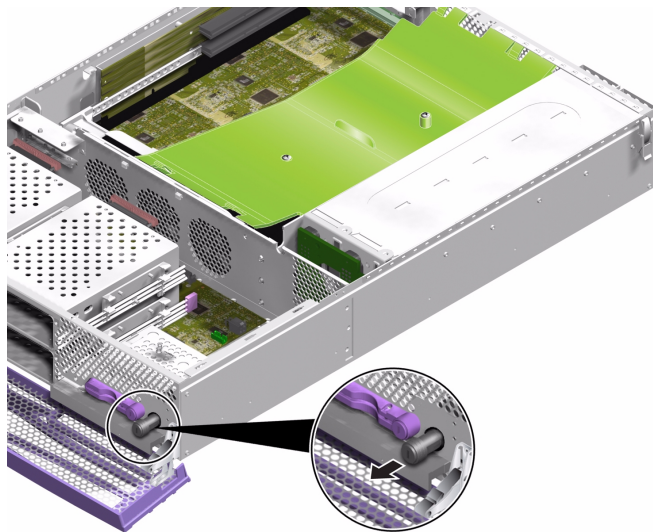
Extracción del ensamblaje de la cerradura de contactos
